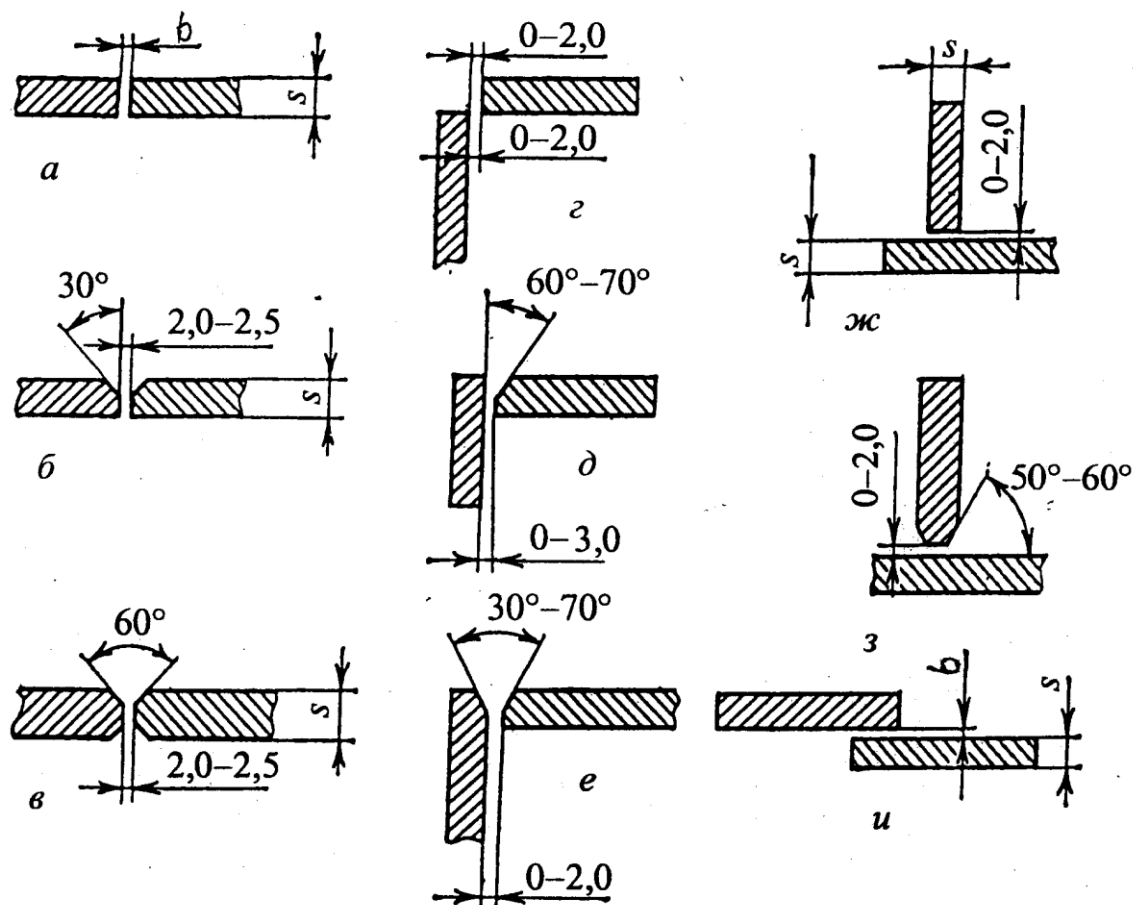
Типы сварных соединений при ручной дуговой сварке
